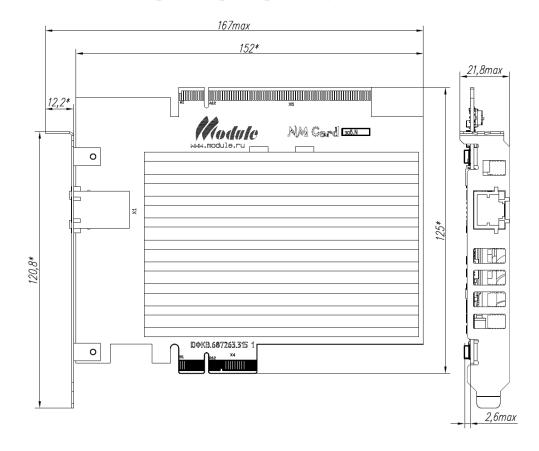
Габаритные размеры Модуля ЮФКВ.469535.002-02
